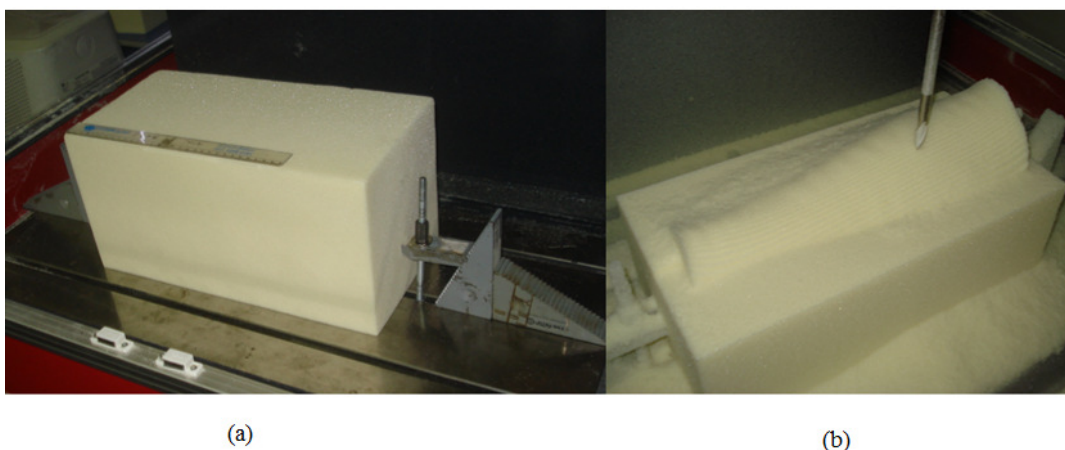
a) Bloco de PU usado como base para a usinagem do perfil da canela b) perfil da perna durante processo de usinagem
